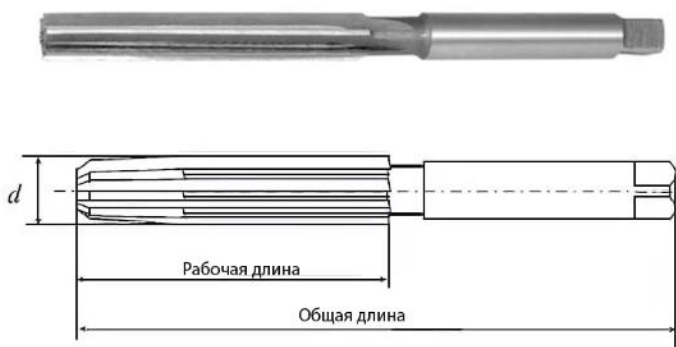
Развертка - режущий инструмент, который нужен для окончательной обработки отверстий после сверления, зенкерования или растачивания
